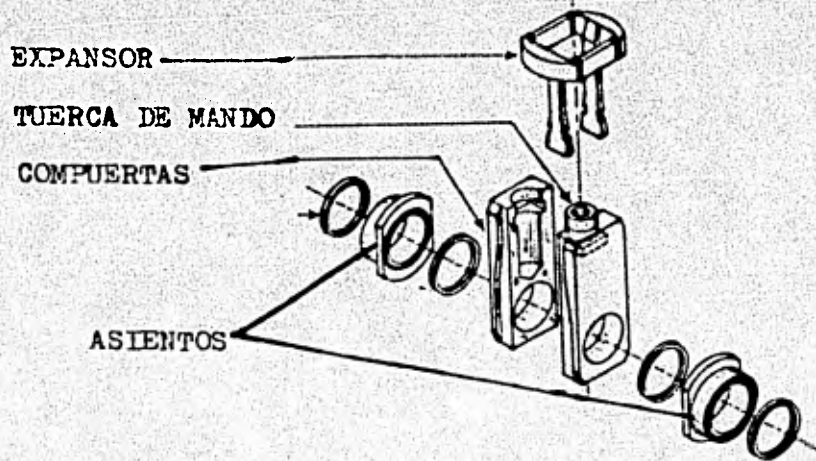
CONJUNTO COMPUERTA - ASIENTOS .
